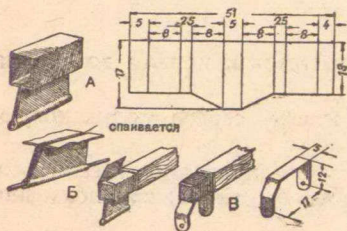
Подшипники: А — развертка подшипника, Б — процесс изготовления, В — подшипник простейшей конструкции.
